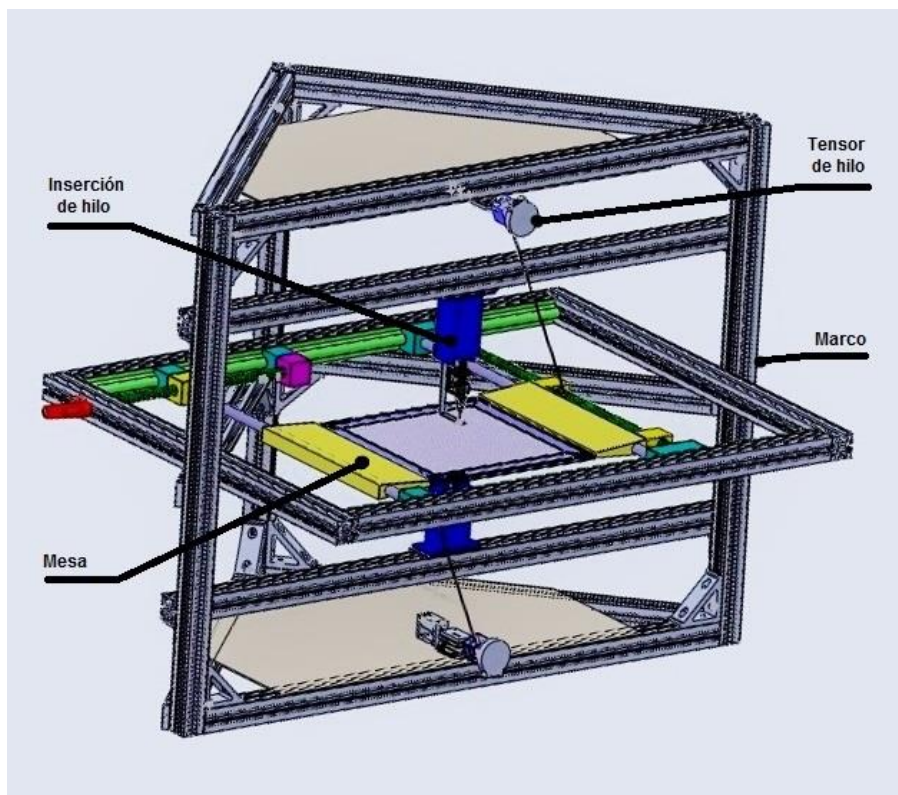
Diseño en CAD del prototipo de máquina y los sistemas que la componen.
